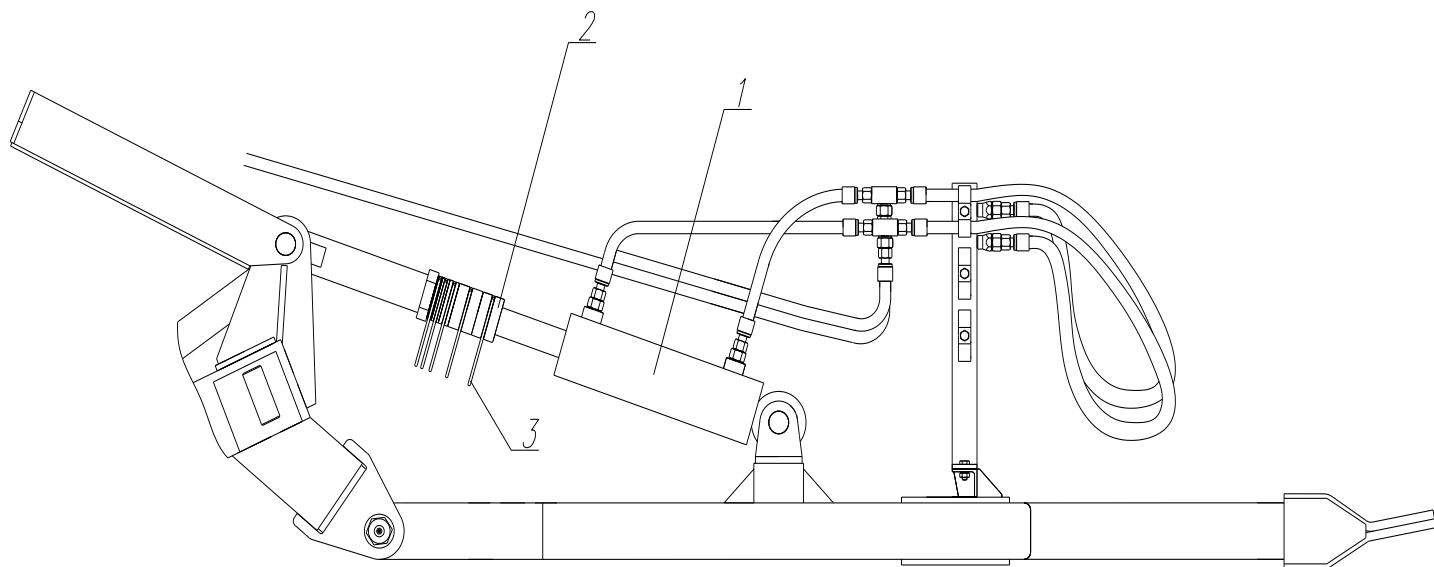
Регулировка заглубления рабочих органов бороны катками
